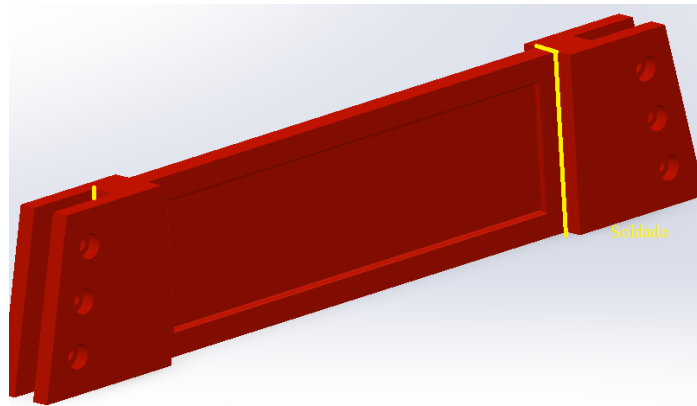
Vista de soldado de pieza N°9.2 (Fuente 97)
